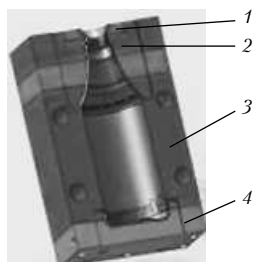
Напівматриця прес-форми для виготовлення об'ємних виробів:
